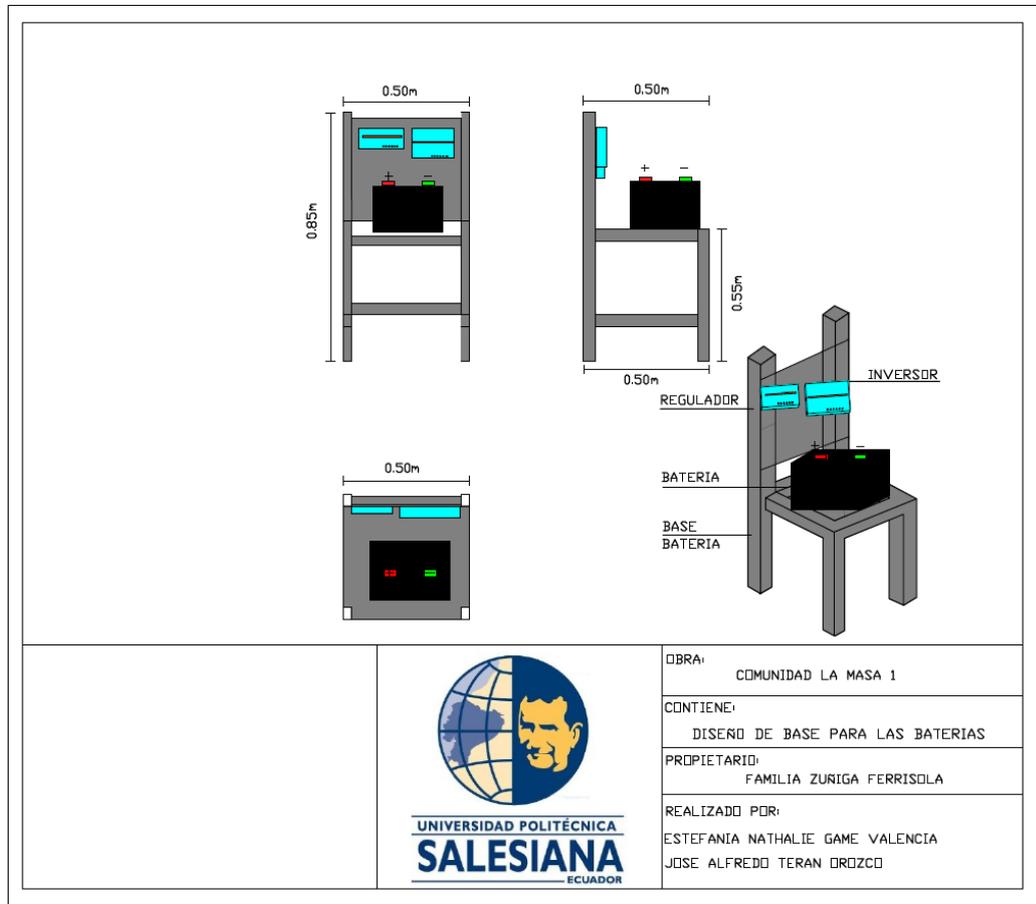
Estructura de base para el banco de baterías del panel solar a instalar en la vivienda (Fuente: Autores).
